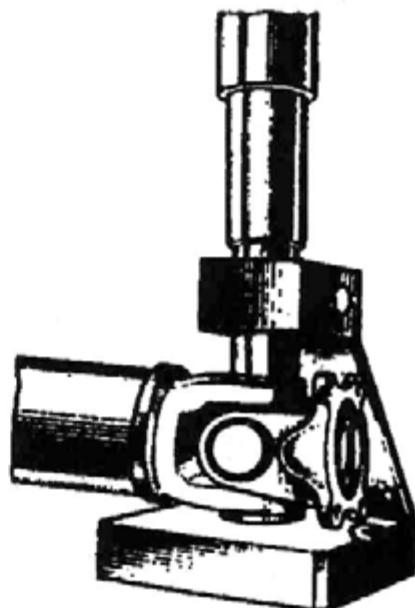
Запрессовка подшипника карданного шарнира с помощью приспособления
